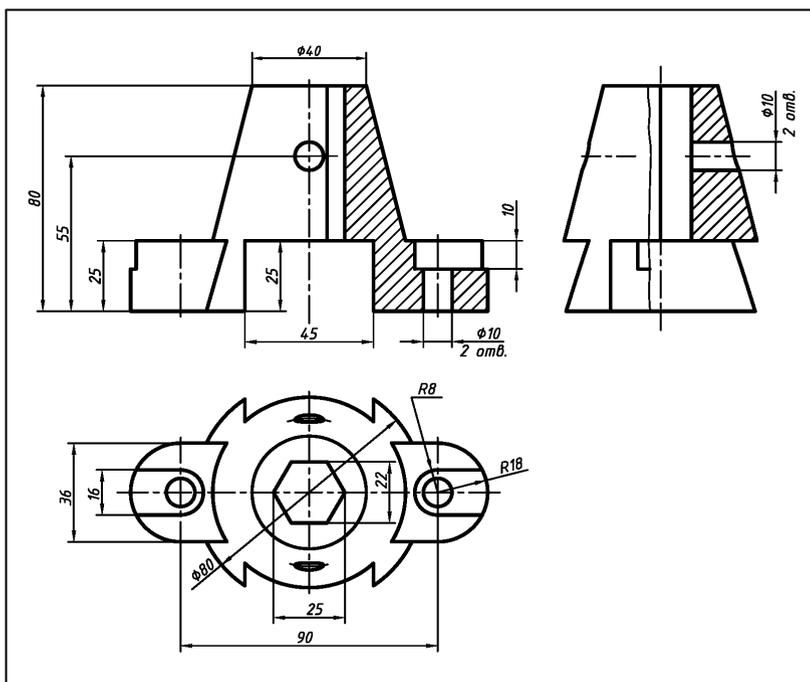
Примеры простановки размеров на учебных чертежах
